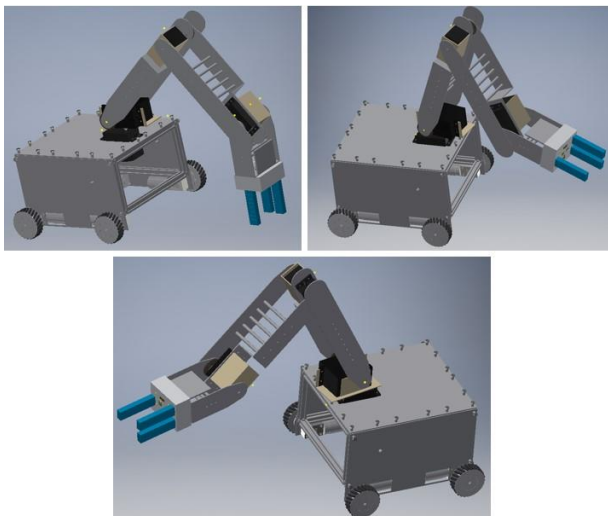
Diseño del robot móvil para remoción de explosivos con la incorporación del prototipo de mano robótica
